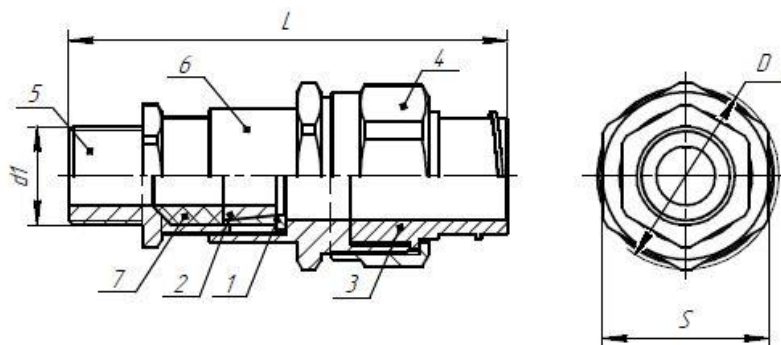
Общий вид кабельного ввода ВА с фитингом для крепления металлорукава.
